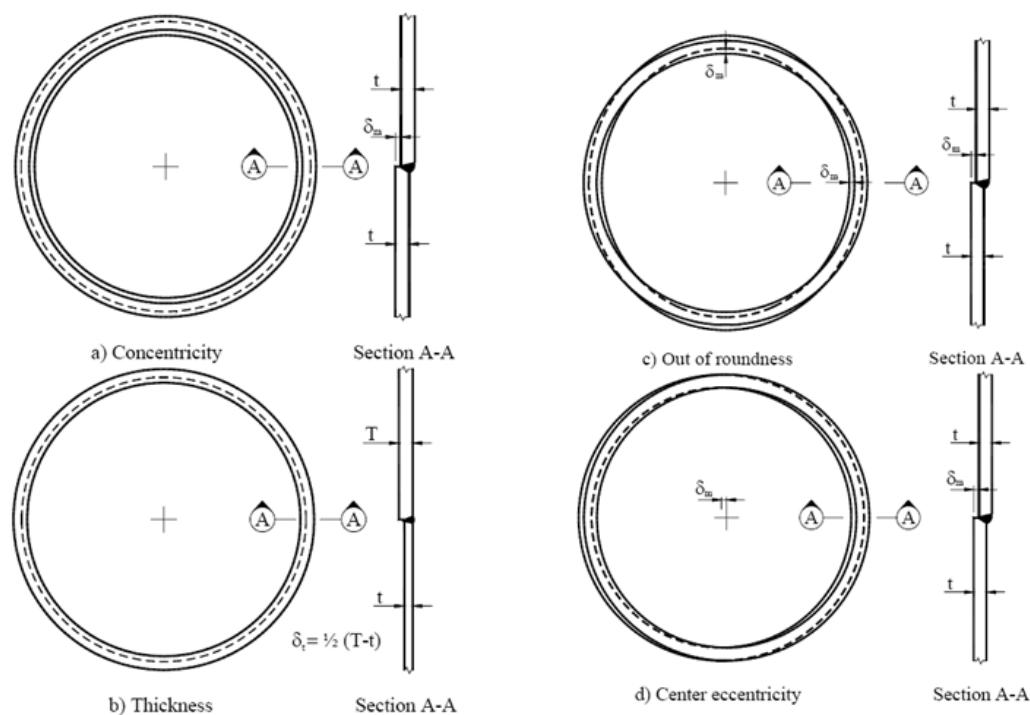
Principais causas do efeito do SCF em estruturas tubulares soldadas [10]
